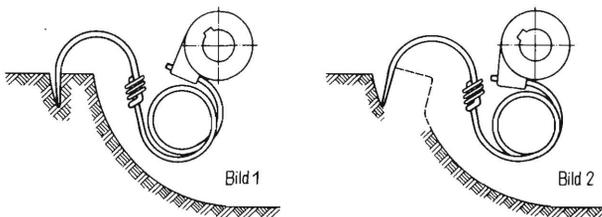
und 2. Fräs Werkzeug nach von Meyenburg.
